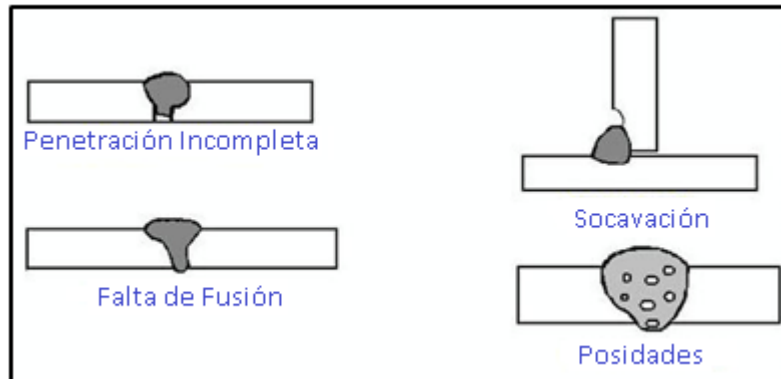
Defectos en Soldadura (<http://www.mailxmail.com>)
